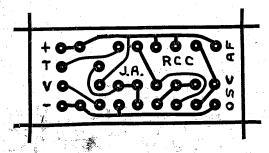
Dessin du circuit imprimé côté cuivre.
